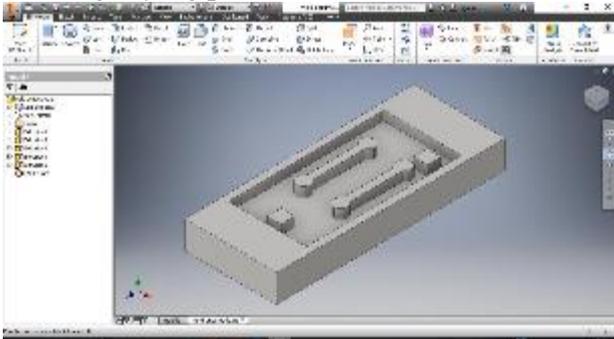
CAD Pneumatic Channel Bentuk Jadi
